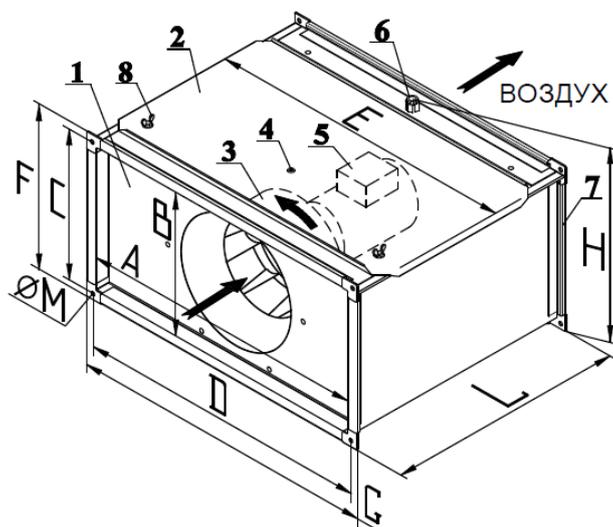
Внешний вид и основные размеры вентиляторов VL
